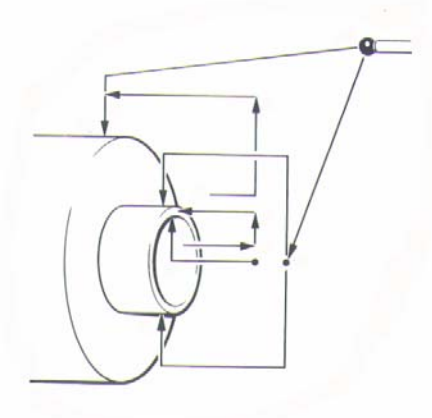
Циклы измерения детали на токарном станке с ЧПУ
